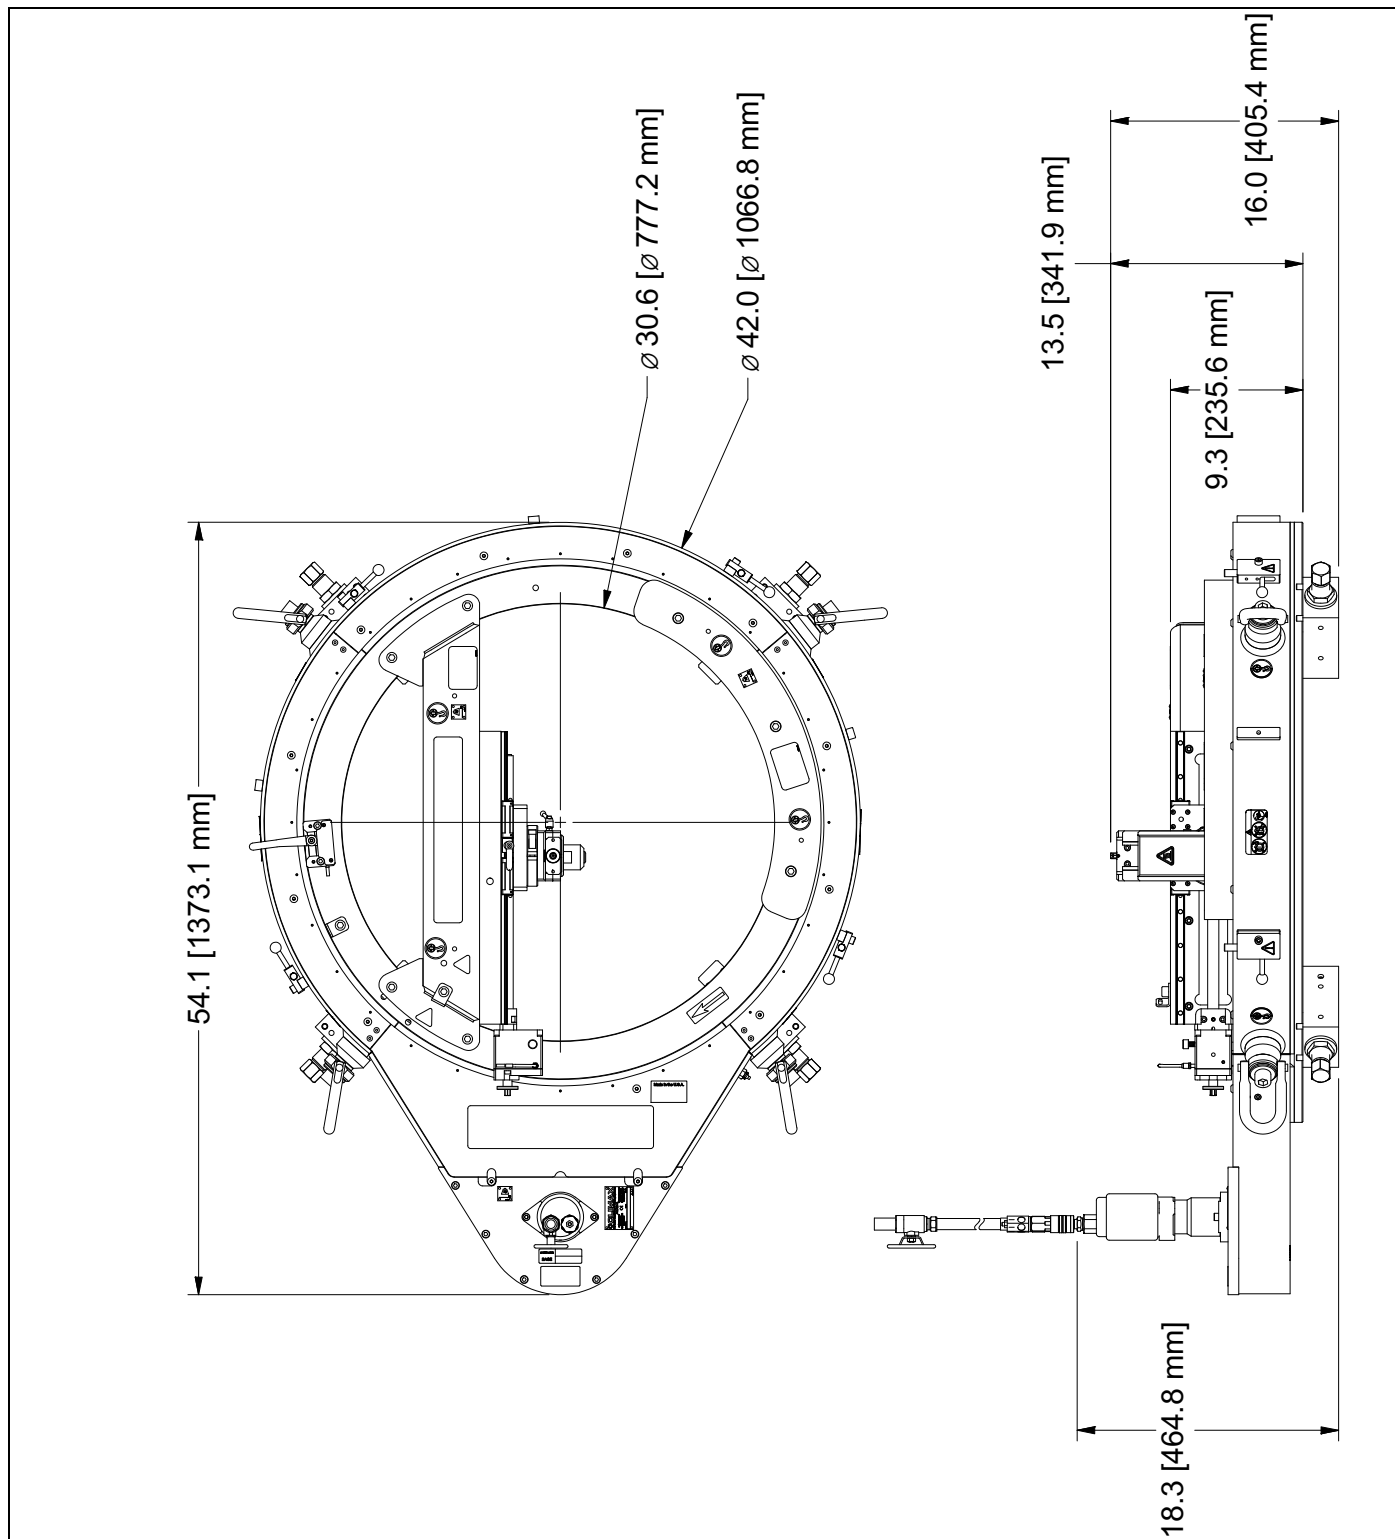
DIMENSIONES DE ODF30 SPEED FACER (N/P 88930)
